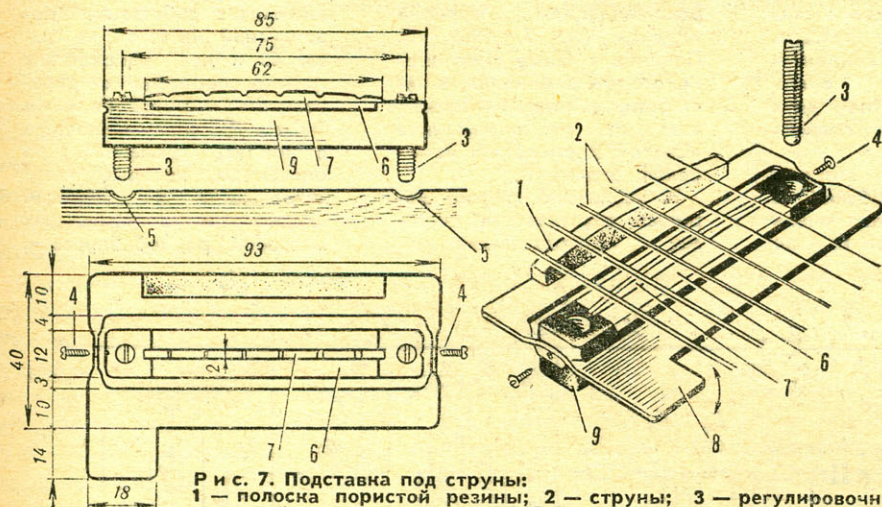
Подставка под струны: 1 — полоска пористой резины; 2 — струны; 3 — регулировочные винты; 4 — винты-шарниры; 5 — опорные металлические полусферы под регулировочные винты; 6 — декоративные полоски цветного оргстекла; 7 — порожек; 8 — подвижная рамка; 9 — корпус подставки.
